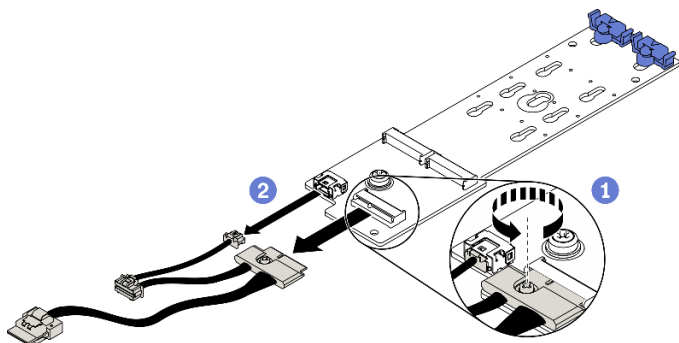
Extracción de los cables M.2 de la placa posterior de M.2
